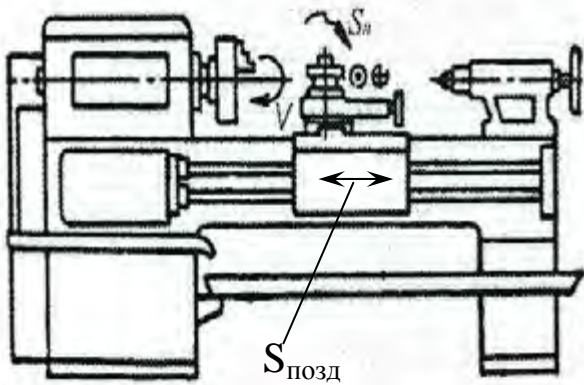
Загальний вид токарно-гвинторізного верстату
